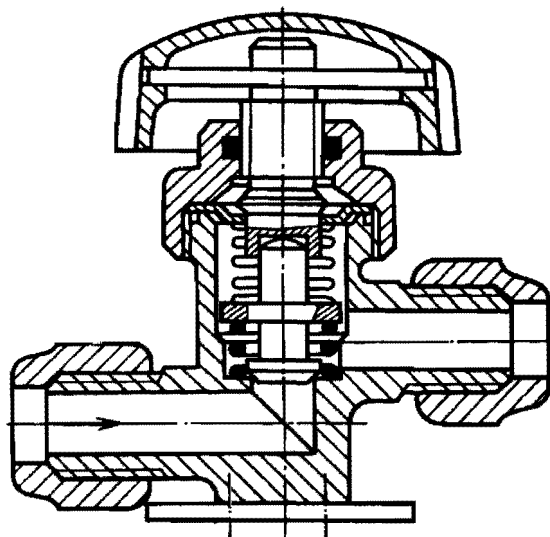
Сильфонный запорный вентиль с присоединением способом отбортовки
